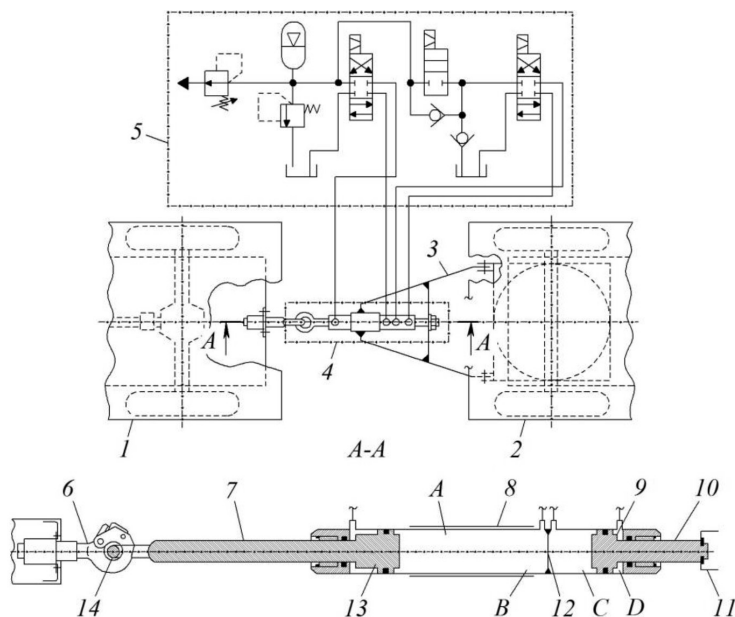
Схема рекуперативного дышла сцепного устройства с функцией самовытаскивания для лесовозного автомобиля с прицепом: 1 – лесовозный автомобиль; 2 – прицеп; 3 – дышло; 4 – гидроцилиндр; 5 – рекуперативный гидропривод управления; 6 – крюк; A, D и B, C – штоковые и поршневые полости гидроцилиндра соответственно; 7, 10 и 9, 13 – штоки и поршни гидроцилиндра соответственно; 8 – корпус дышла; 11 – поперечина дышла; 12 – герметичная перегородка гидроцилиндра; 14 – присоединительное кольцо
